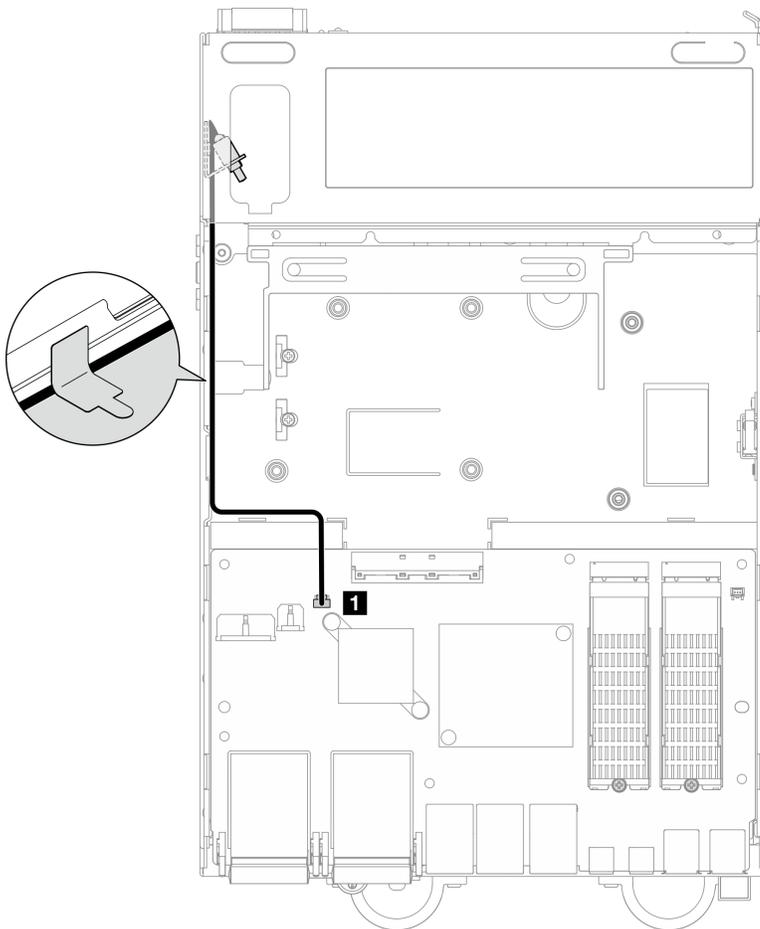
Disposición de los cables del conmutador de posición de bloqueo
